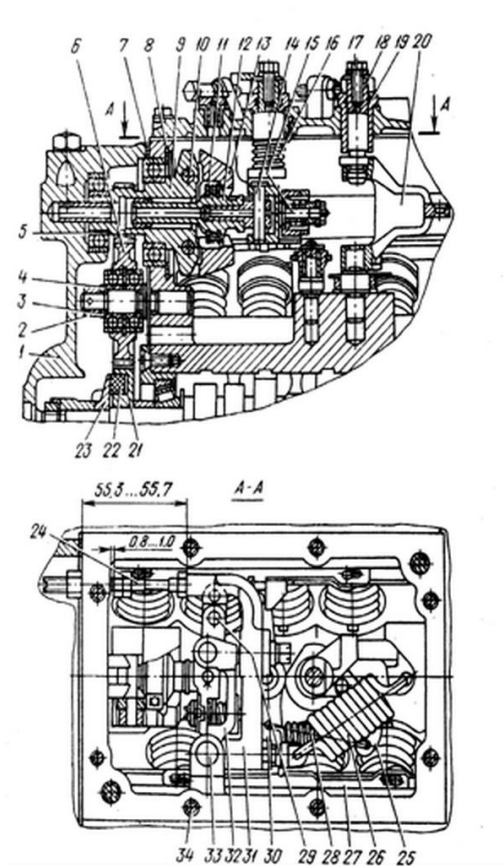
Регулятор частоты вращения: 1 – крышка задняя; 2 – гайка; 3 – шайба; 4 – подшипник; 5 – прокладка регулировочная; 6 – шестерня промежуточная; 7 – прокладка задней крышки регулятора; 8 – кольцо стопорное; 9 – державка грузов; 10 – ось груза; 11 – подшипник упорный; 12 – муфта; 13 – груз; 14 – палец; 15 – корректор; 16 – пружина возвратная рычага останова; 17 – болт; 18 – втулка; 19 – кольцо; 20 – рычаг пружины регулятора; 21 – шестерня ведущая; 22 – сухарь ведущей шестерни; 23 – фланец ведущей шестерни; 24 – болт регулировочный подачи топлива; 25 – рычаг стартовой пружины; 26 – пружина регулятора; 27 – рейка; 28 – пружина стартовая; 29 – штифт; 30 – рычаг реек; 31 – рычаг регулятора; 32 – рычаг муфты грузов; 33 – ось рычагов регулятора; 34 – болт крепления верхней крышки
